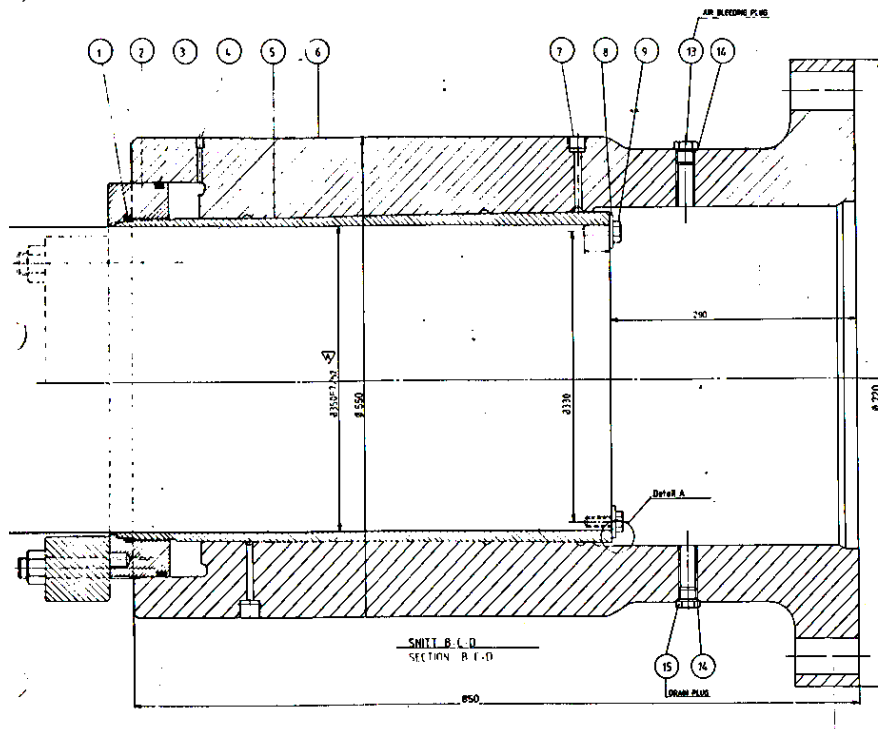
Сборочный (монтажный) чертеж посадки полумуфты на гребной вал
